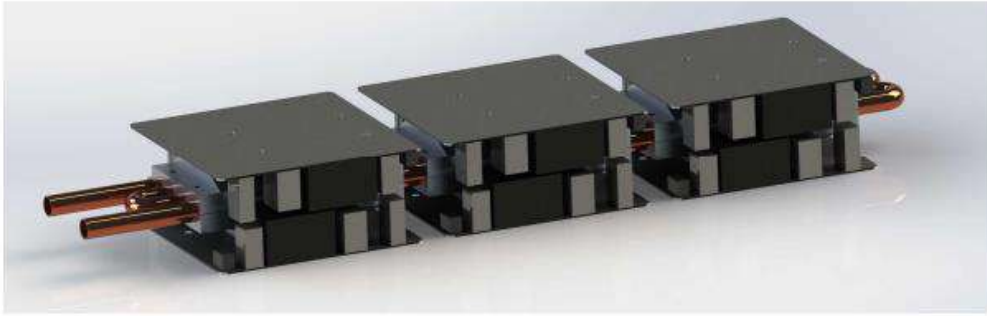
Module de 6 cartes mères de chauffage, jusqu'à 4 par chaudière numérique
